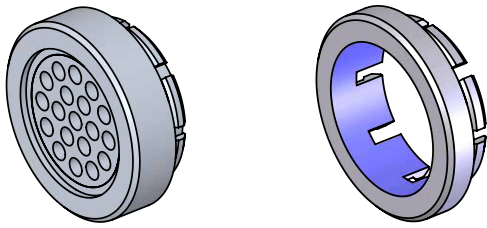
Patentierter Flammenschutz Typ 6539A1Q01, Membranschutzing Typ 6539A2 (beide werkzeuglos montierbar)
